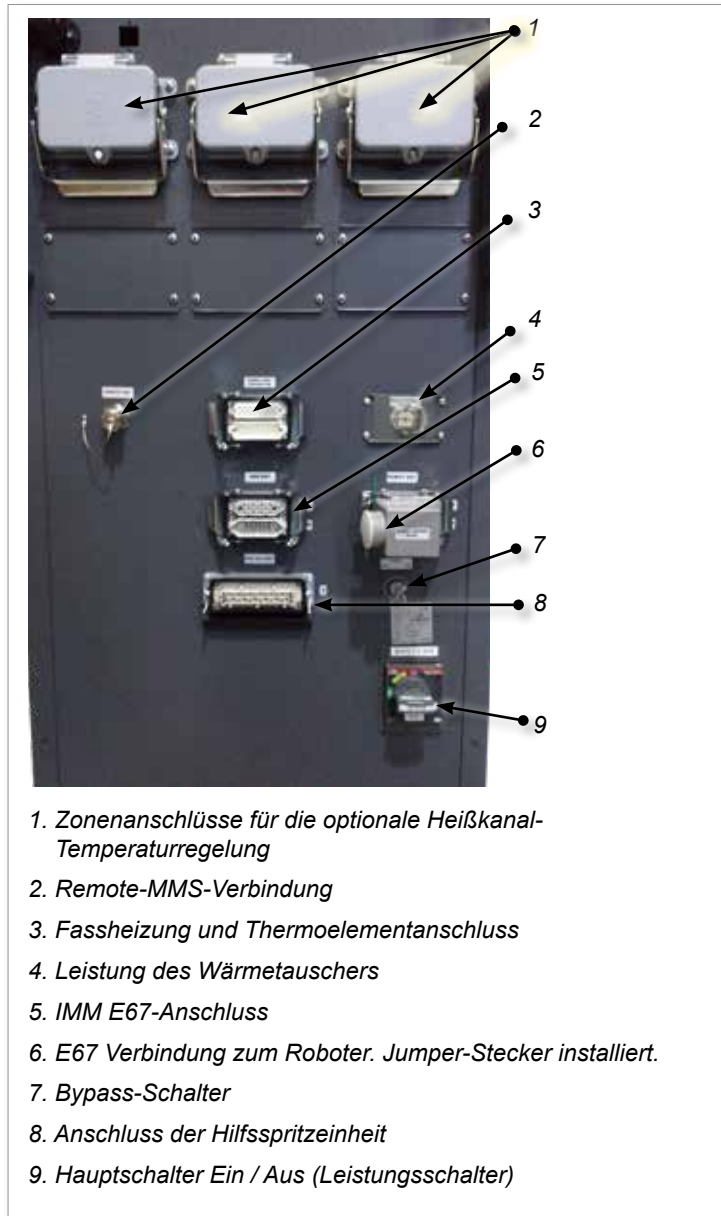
Rückseitige Anschlüsse des Steuergeräts
